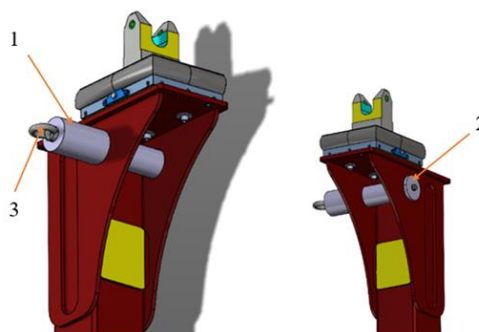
Dispositivo de elevação dos braços B102 e B103.
